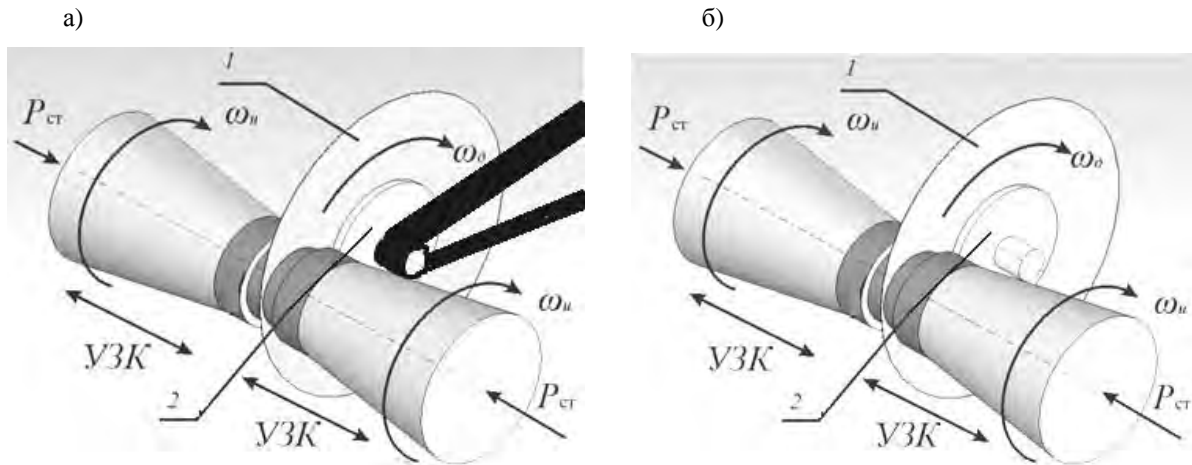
Технологическая схема шаржирования распиловочных дисков с ультразвуком по двухсторонней схеме: а – с вращением заготовки диска от отдельного привода; б – с вращением заготовки диска за счет фрикционной торцевой передачи
